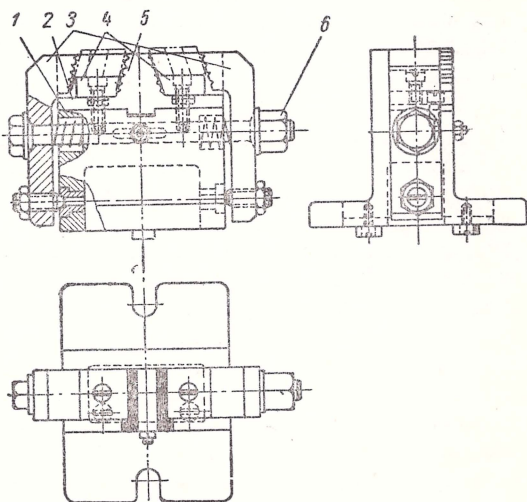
Приспособления для обработки ножей к сборным фрезам
